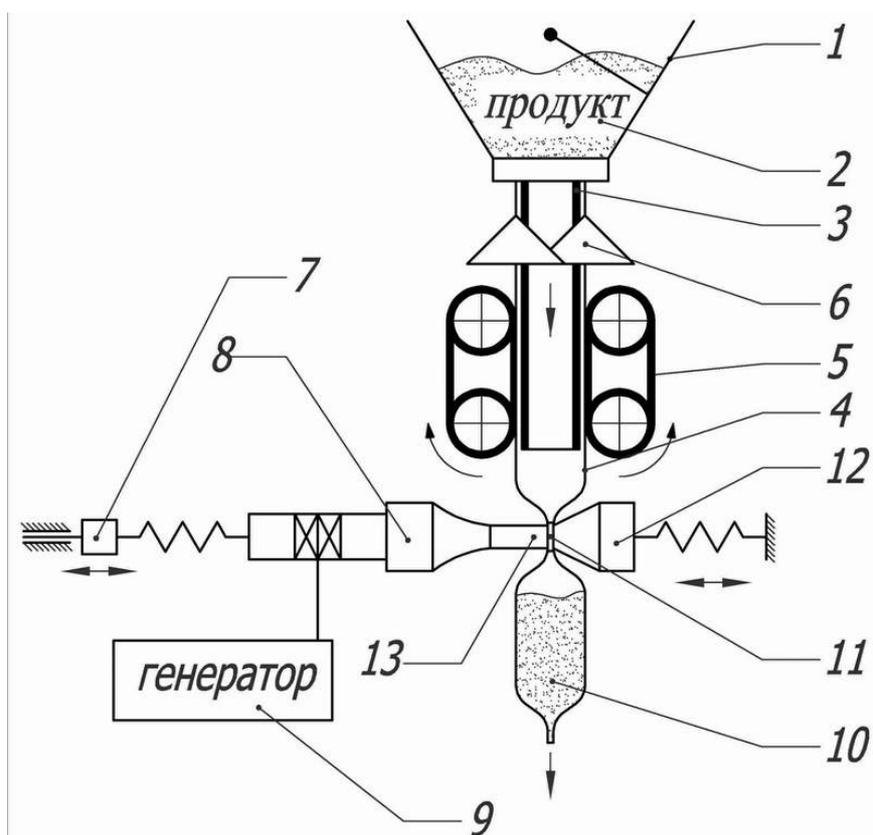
Схема формирования поперечного герметизирующего шва ультразвуковой сваркой
